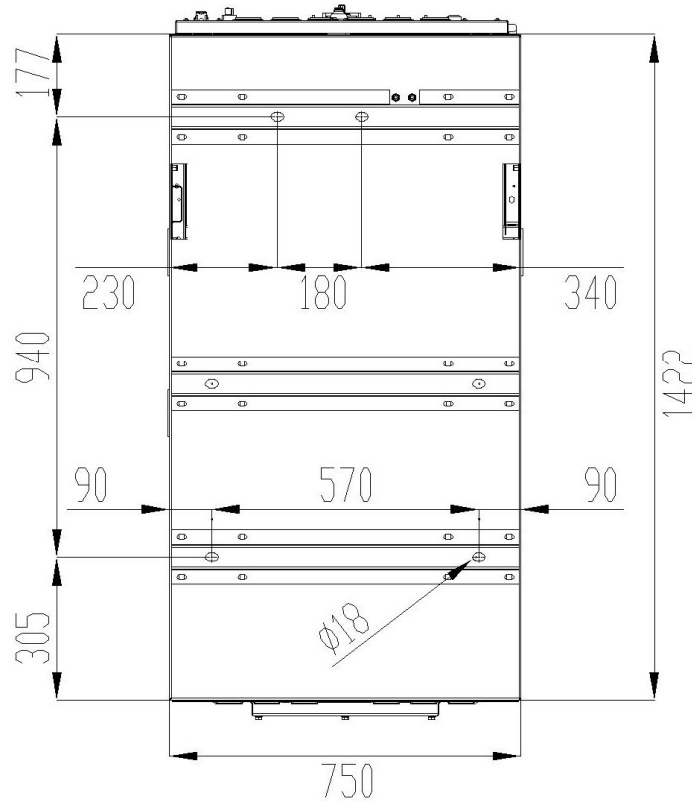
Отвори під анкерні кріплення на дні КМ-1Ф
